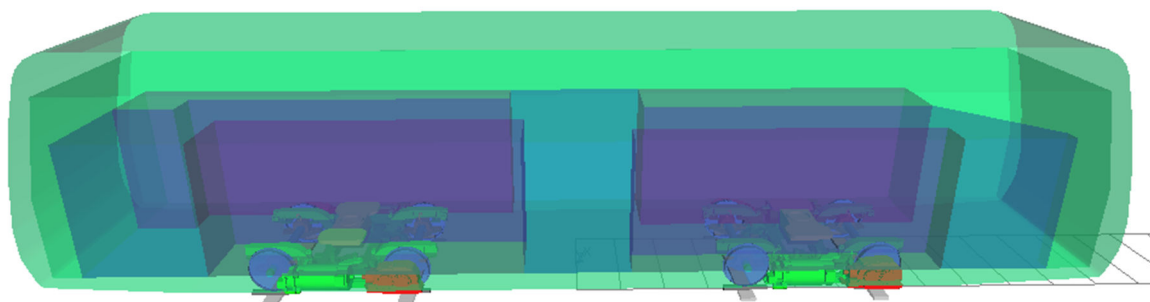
CAD model skříně tramvaje s otočnými podvozky
